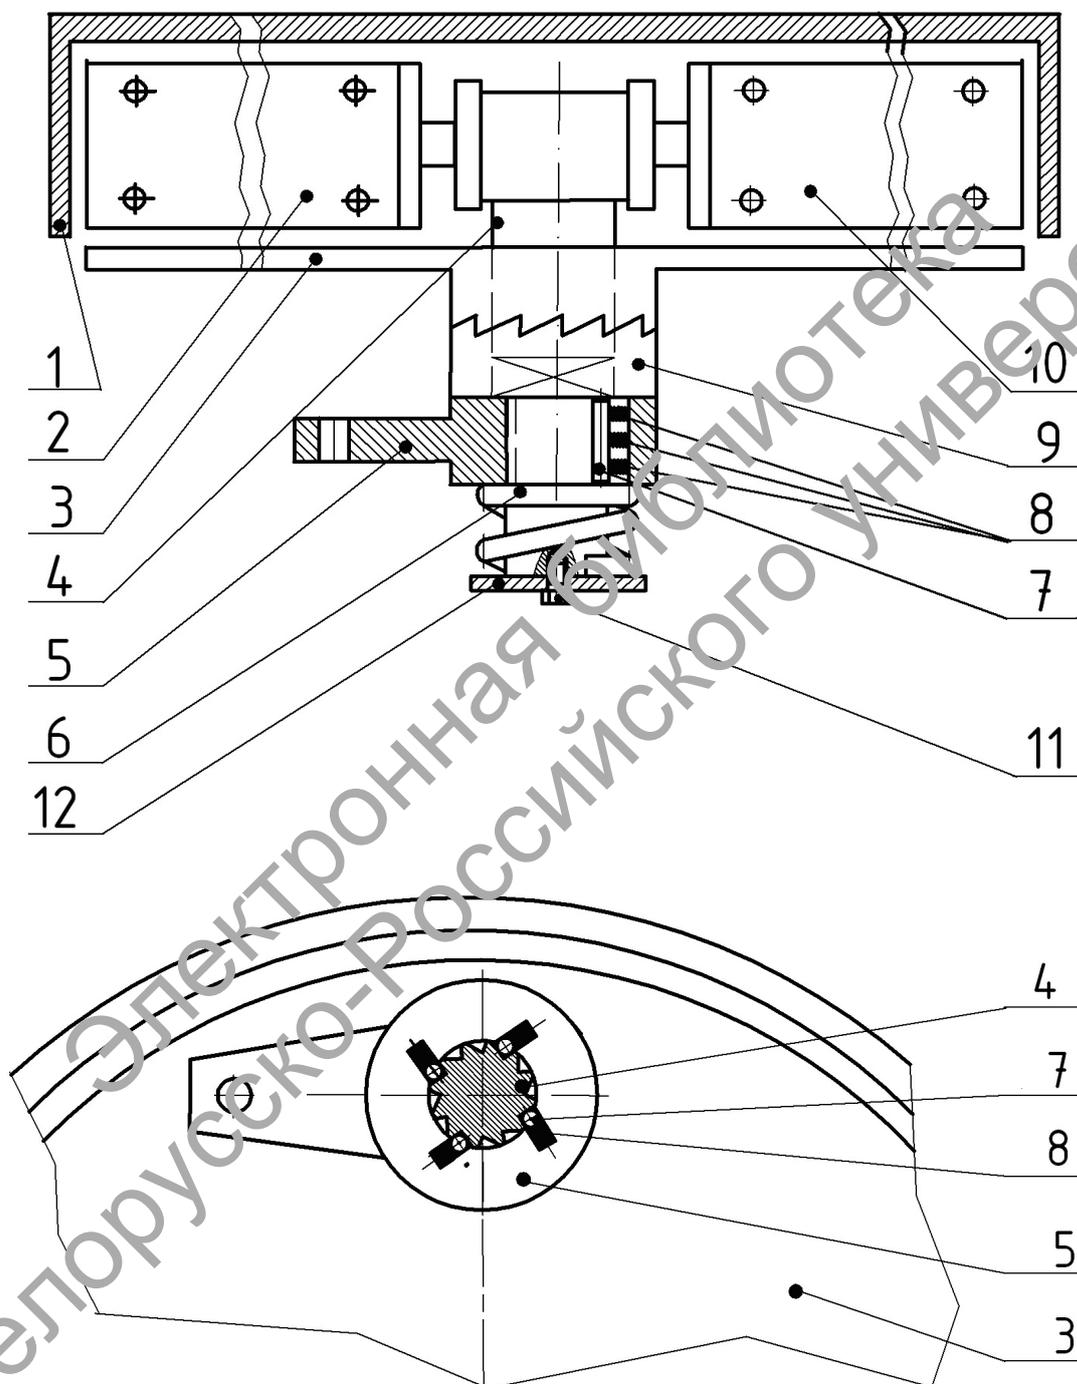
Автоматический регулятор зазора между тормозными колодками и тормозным барабаном колесного тормозного механизма [7]: 1 – барабан; 2 – колодка; 3 – щит тормозной; 4 – вал; 5 – рычаг; 6 – пружина; 7 – ролики; 8 – пружина; 9 – втулка; 10 – колодка; 11 – винт; 12 – шайба
